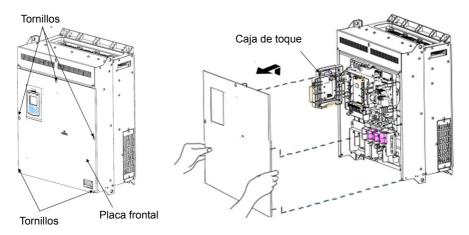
Extracción de la placa frontal y de la placa del cableado (FRN110AQ1S-4□)
